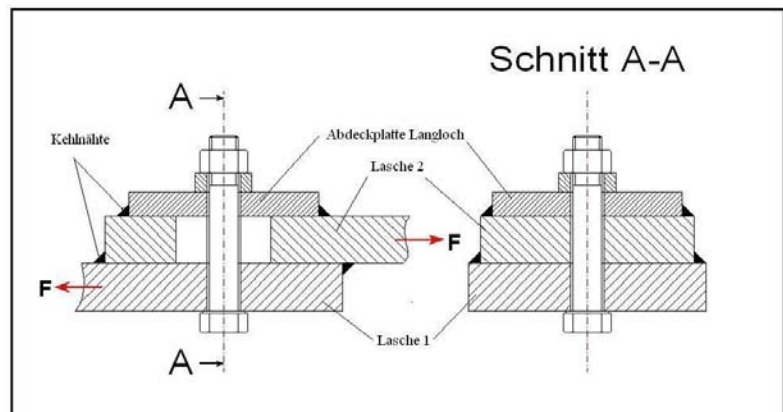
/ Schnitt - Sicherung und Kraftübertragung durch Schweißnähte
